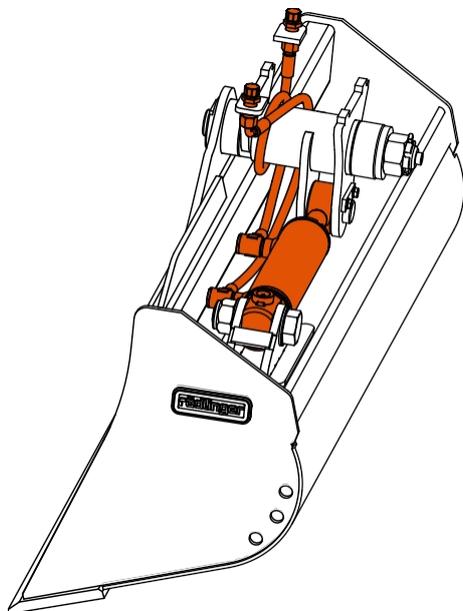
Cuchara de limpieza de zanjas con cilindro hidráulico sin soporte de cuchara y placa de suspensión trasera
